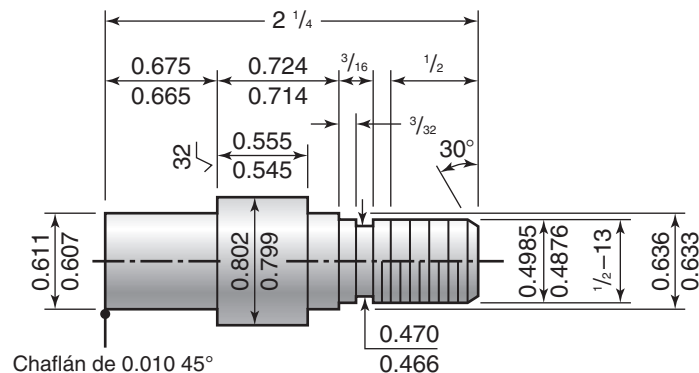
Parte maquinada y roscada que muestra diversas dimensiones y tolerancias; todas las dimensiones se miden en pulgadas. Obsérvese que algunas tolerancias sólo son de algunas milésimas de pulgada.
